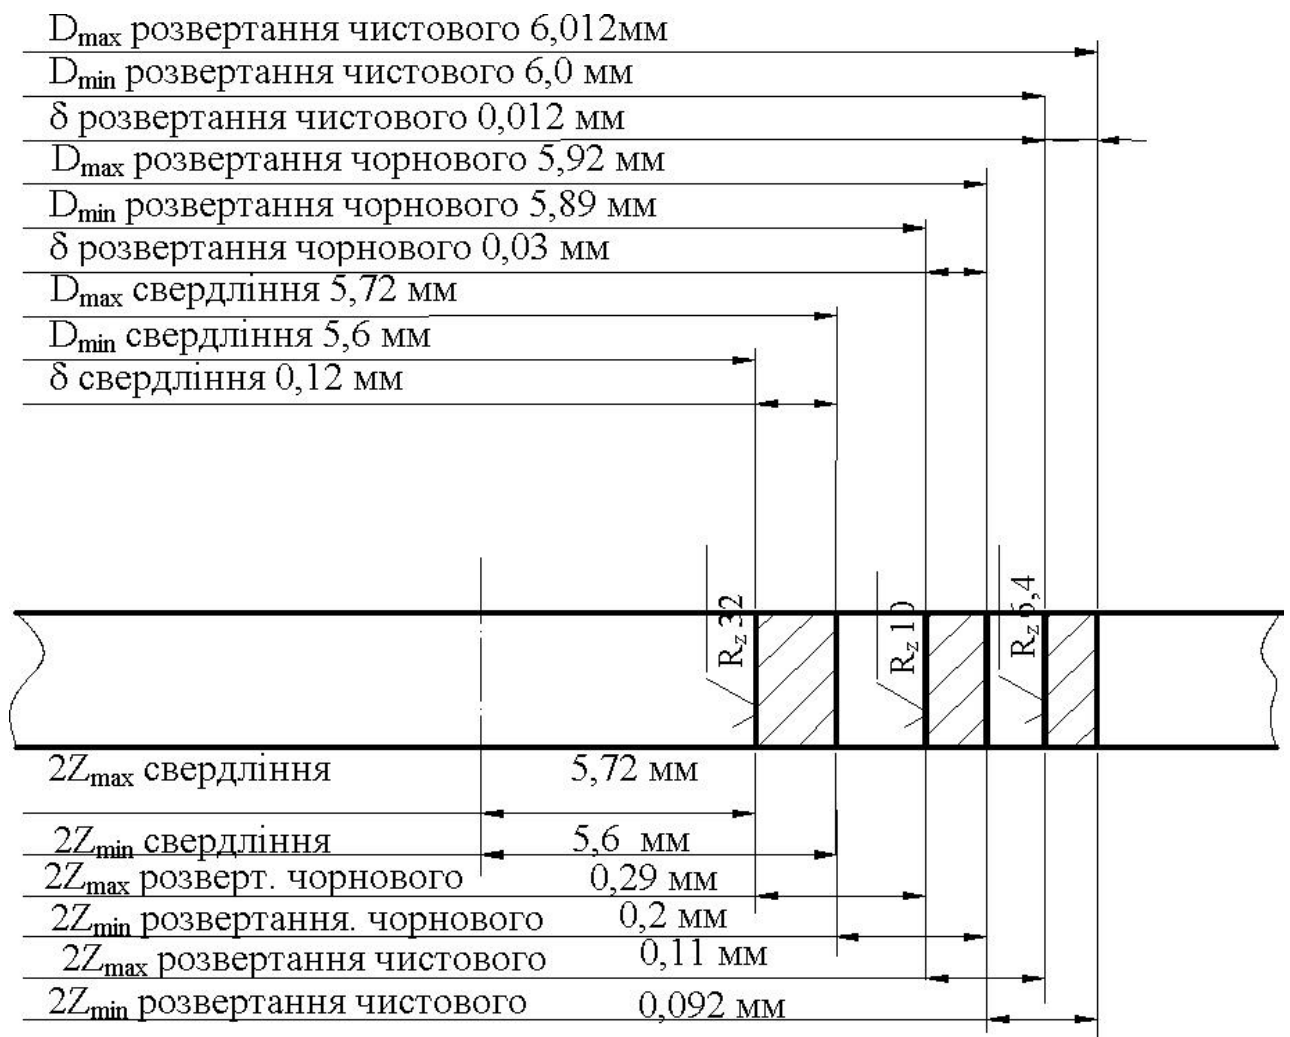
Розташування припусків для оброблення отвору $\varnothing 6H7$ методами свердління, розвертання чорного та розвертання чистового
